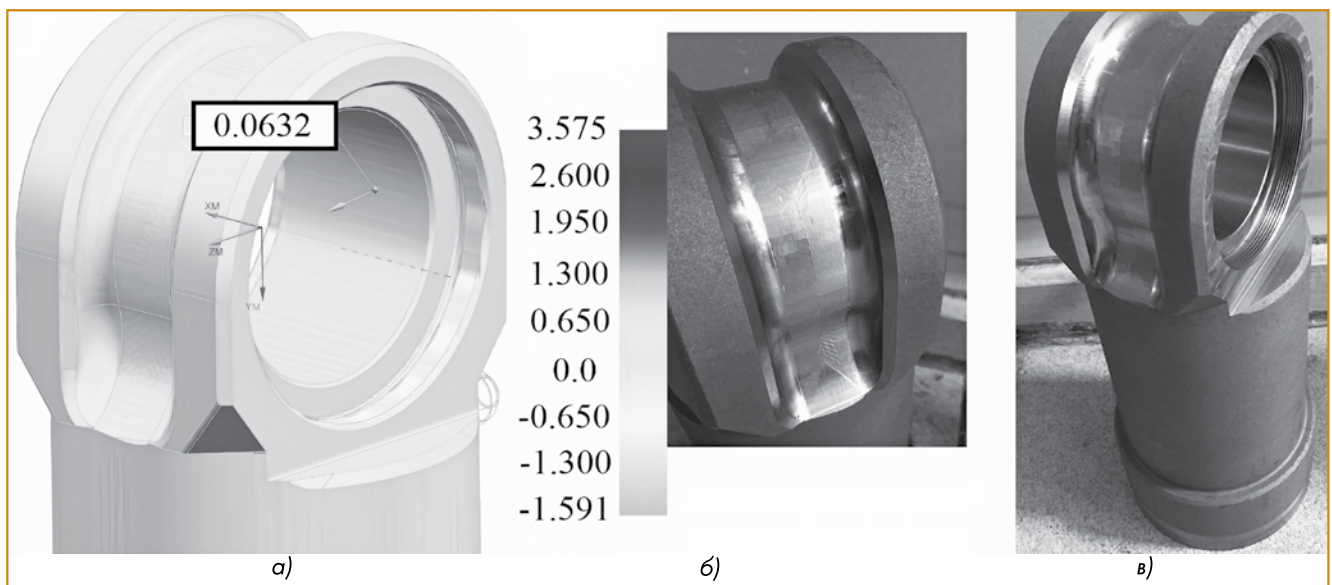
Обработанная деталь «Корпус»: а) в системе NX, б) на обрабатывающем центре
